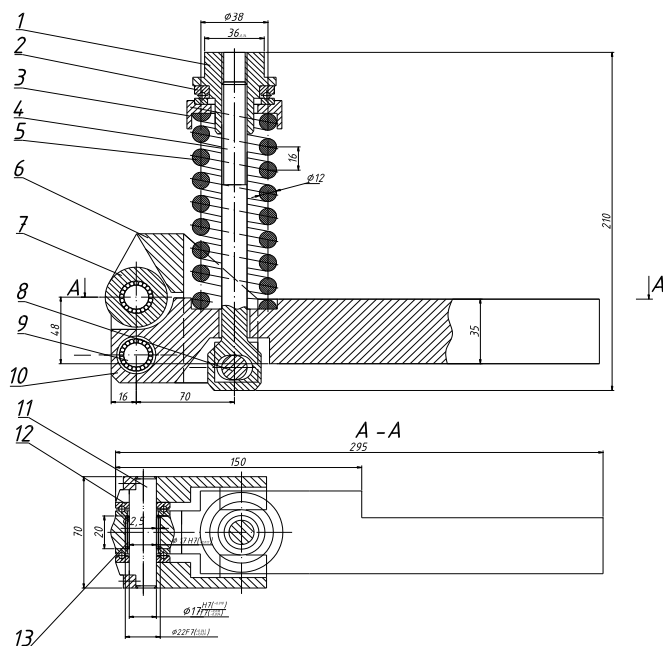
Конструктивная схема устройства для обкатывания деталей торообразным роликом со стабилизацией рабочего усилия обкатывания
